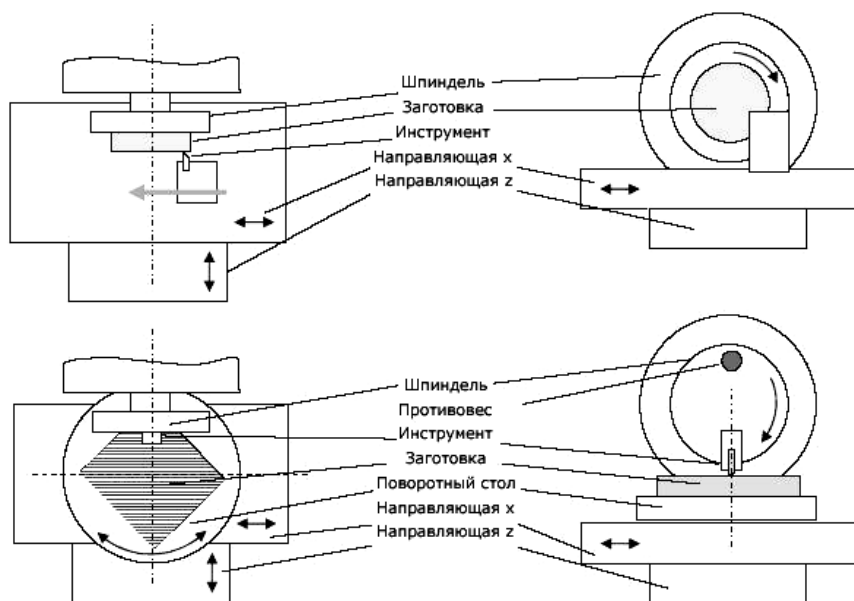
Схемы процессов механической обработки офтальмологических изделий и матриц для их формования:
